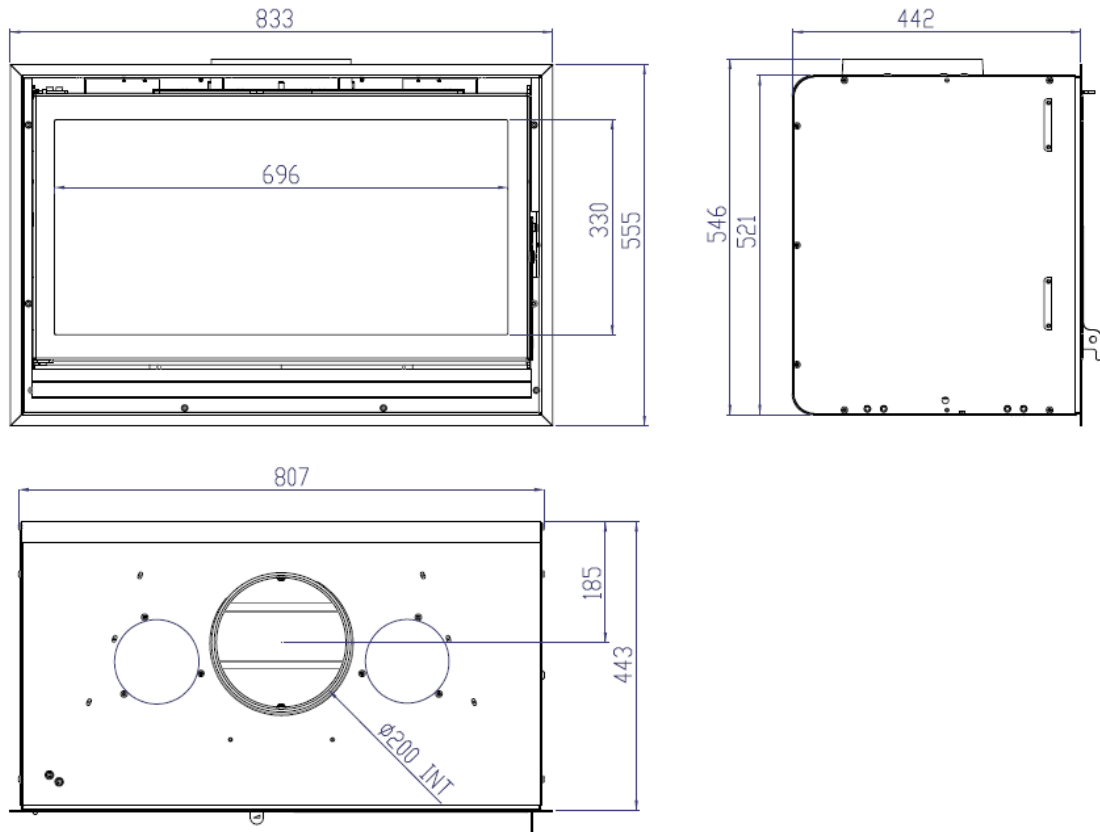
Dimensiones en mm del aparato SANTANDER
